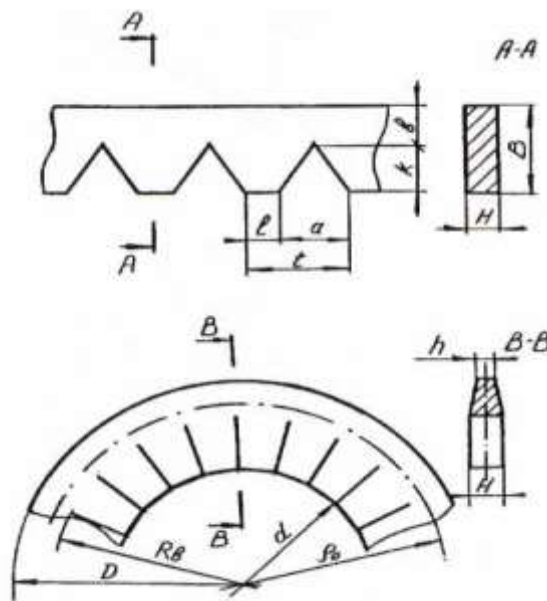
Схеми заготовки для навивання ширококутових спіралей до і після формоутворення
